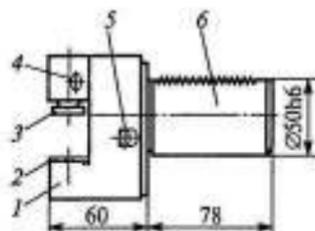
Резцовый блок с цилиндрическим хвостовиком:
